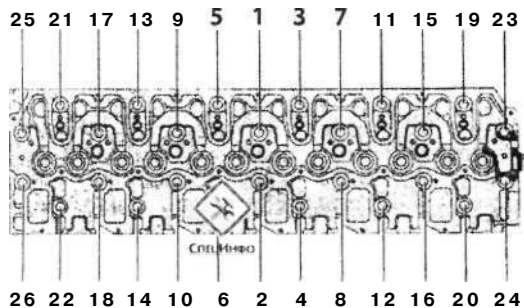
Порядок затяжки болтов головки блока цилиндров.
